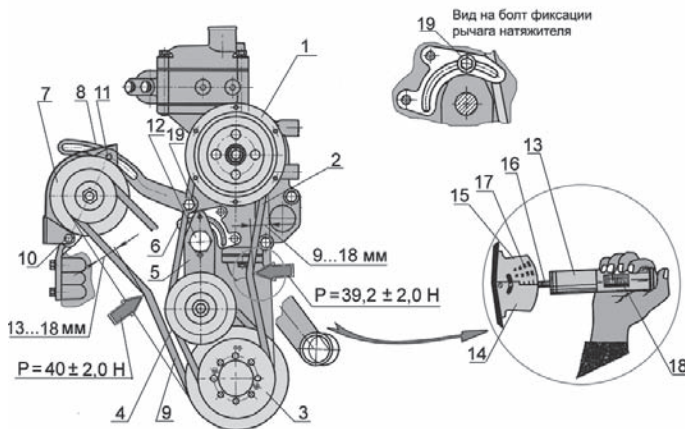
Проверка натяжения ремней. 1 - шкив водяного насоса; 2 - клиновой ремень привода водяного насоса; 3 - шкив коленчатого вала; 4 - шкив натяжной; 5 - рычаг натяжителя; 6 - планка; 7 - генератор; 8 - планка; 9 - клиновой ремень привода генератора; 10 - болты с гайками (крепления лап генератора); 11 - болт (крепления генератора к планке); 12 - болт центральный (крепления рычага натяжителя); 13 - корпус ручки устройства КИ-8920; 14 и 15 сегменты; 16 - шток; 17 - шкала прогиба; 18 - указателя нагрузки; 19 - болт фиксации рычага натяжителя.
